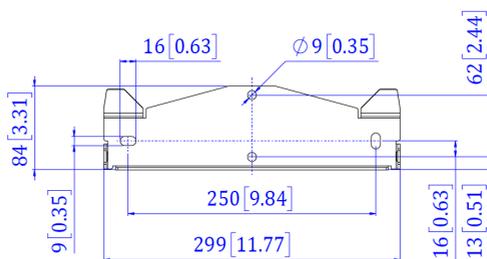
Dimensioni della staffa di montaggio dell'inverter
